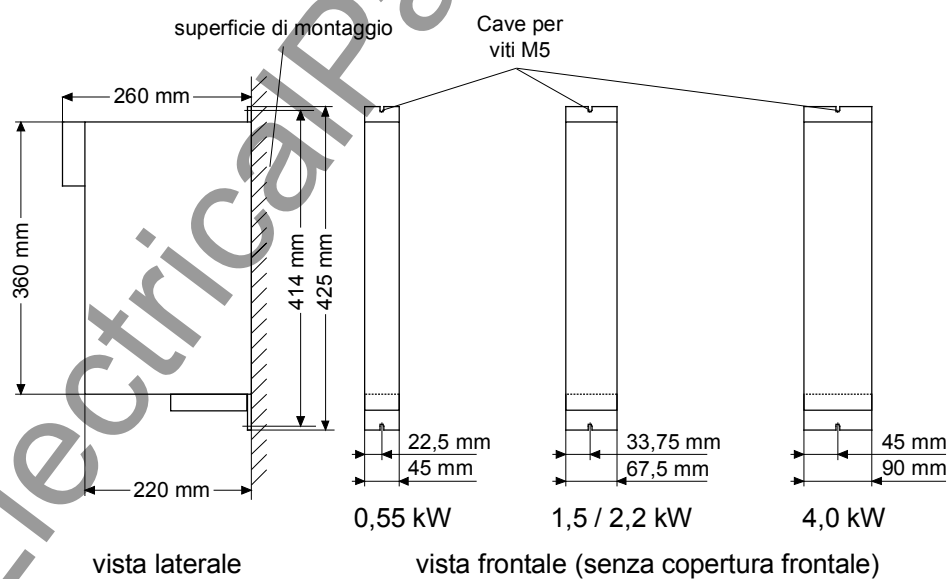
Disegni d'ingombro per larghezza custodia fino a 90 mm
